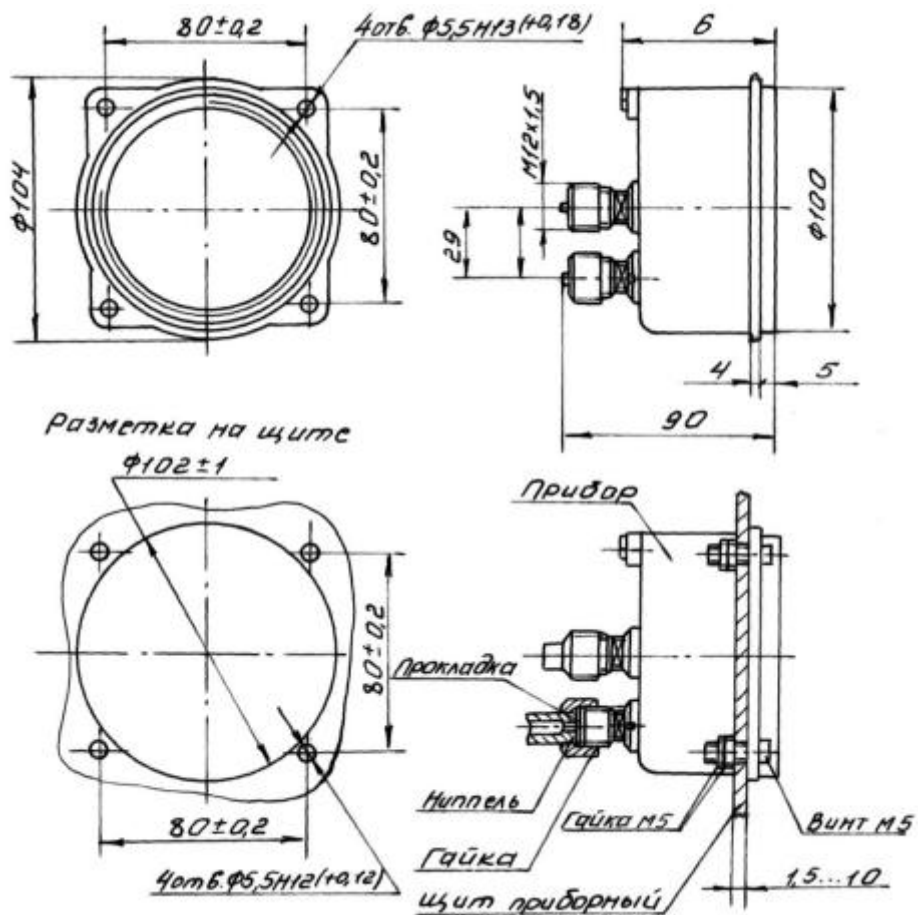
Габаритные и присоединительные размеры прибора с радиальным исполнением штуцера
